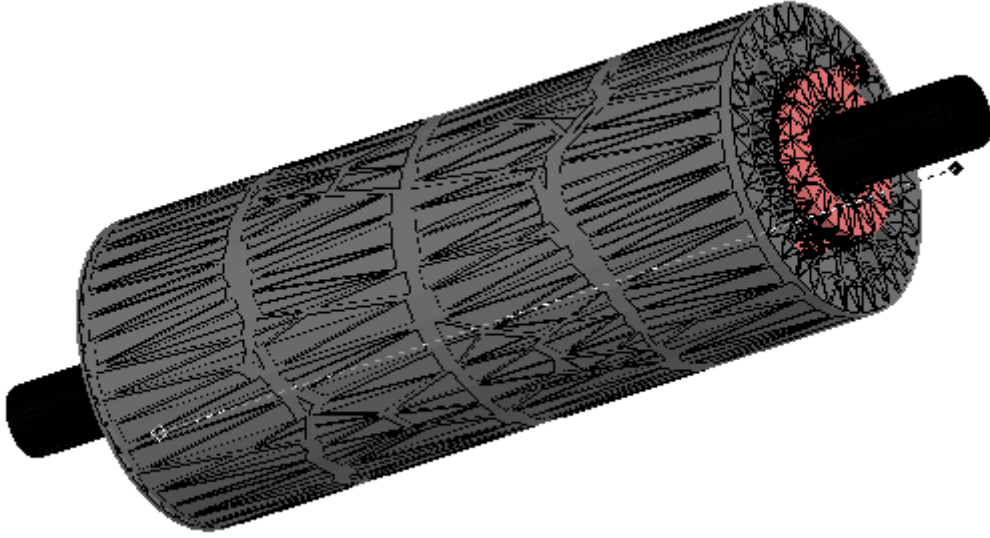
Asenkron Motorun 3 Boyutlu Rotor Durumu
